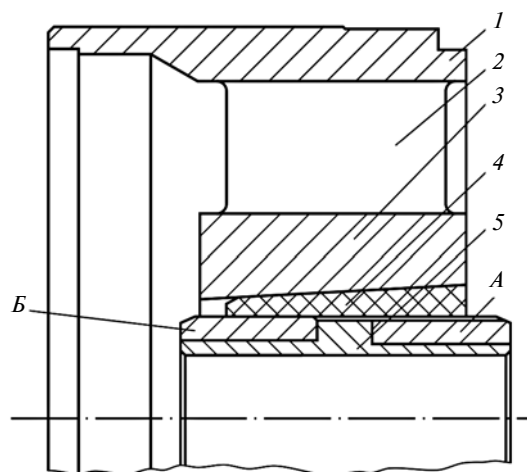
Радиальный подшипник скольжения со втулкой-вкладышем, изготовленной из спечённого порошкового материала с высокомолекулярным связующим из термопластичного полимера:
